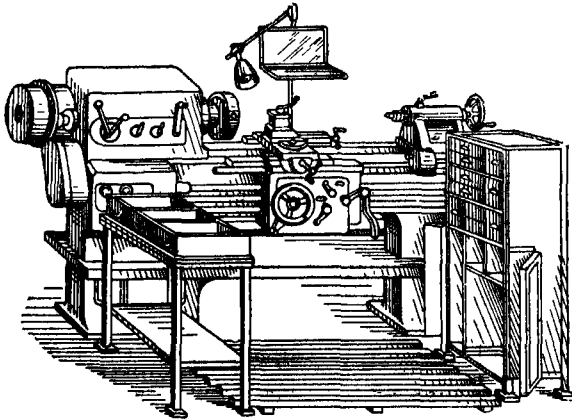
Типовая планировка рабочего места токаря: 1—приемный столик для деталей; 2—станок; 3—инструментальный шкаф; 4—подножная решетка.
